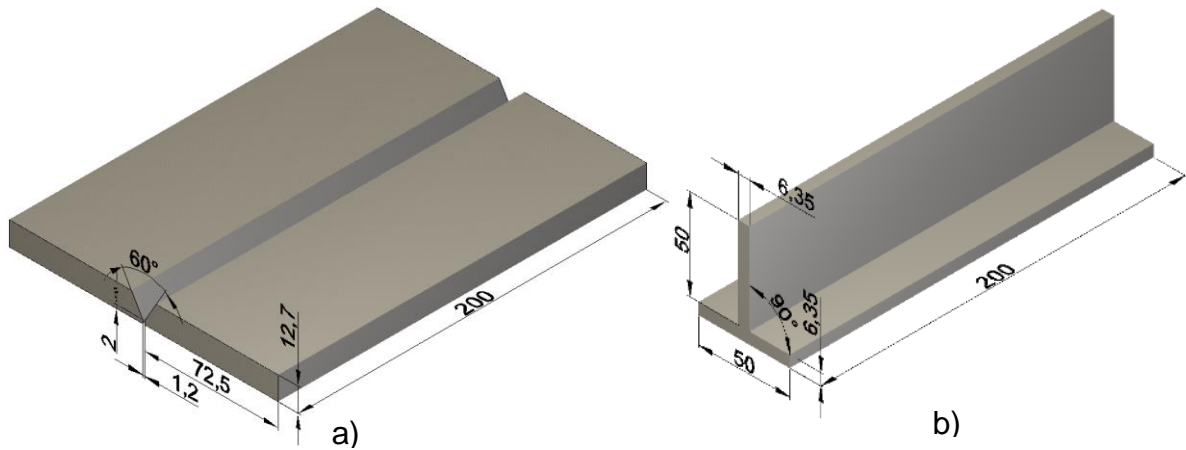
Dimensões e geometrias das juntas: a) de topo com chanfro “V”; b) de ângulo em “T”.
